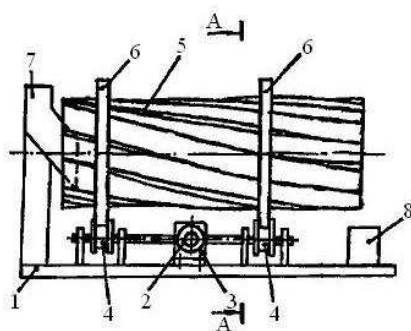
Барабанный смеситель кормов, вид спереди
